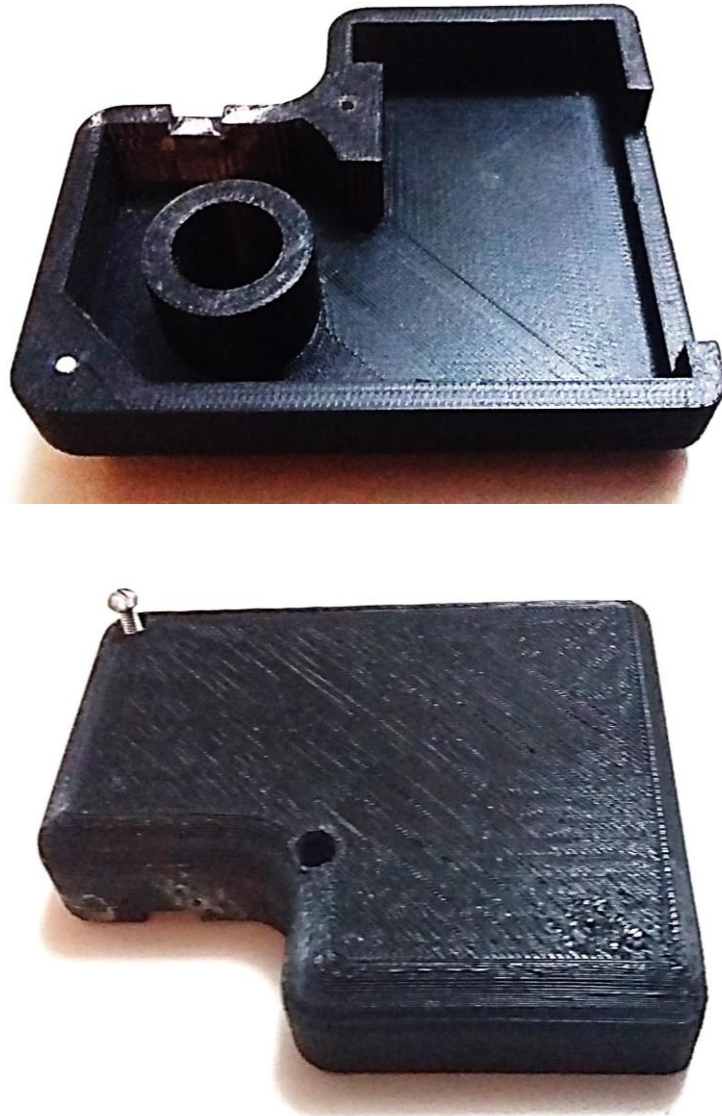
Carcasa parte Izquierda manufacturara en impresión de prototipos rápidos 3D.
